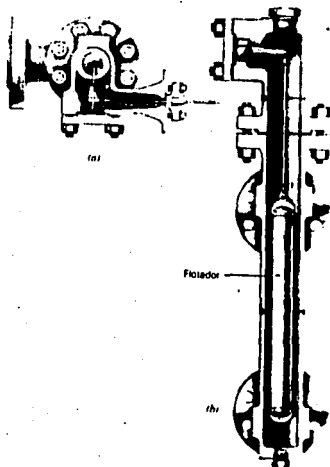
Flotador: a) Vista Superior, b) Vista Lateral
